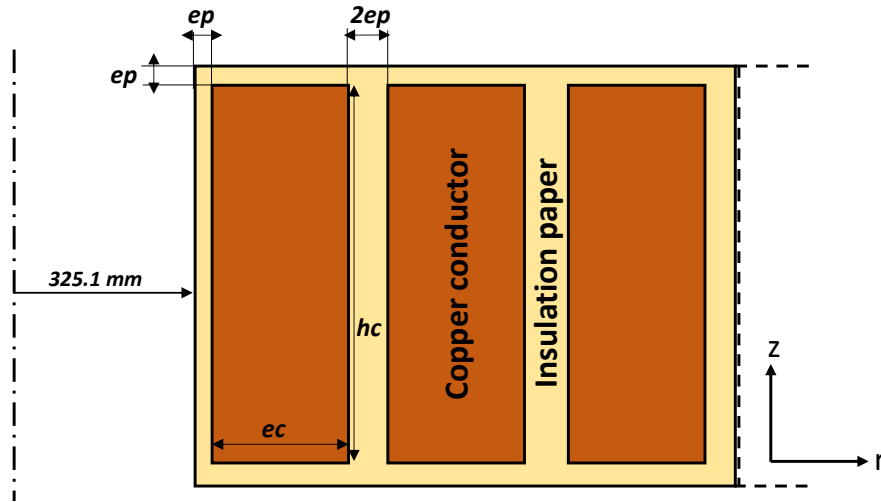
Vue en coupe d'un disque d'enroulements [85].
